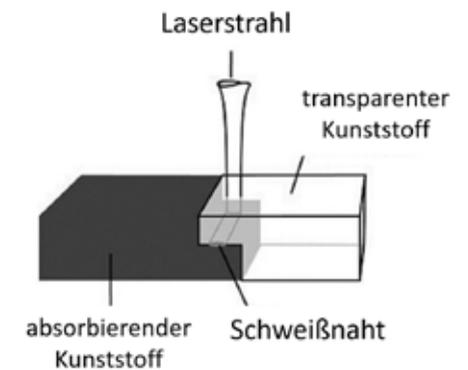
Prinzip des Laserdurchstrahlschweißens
